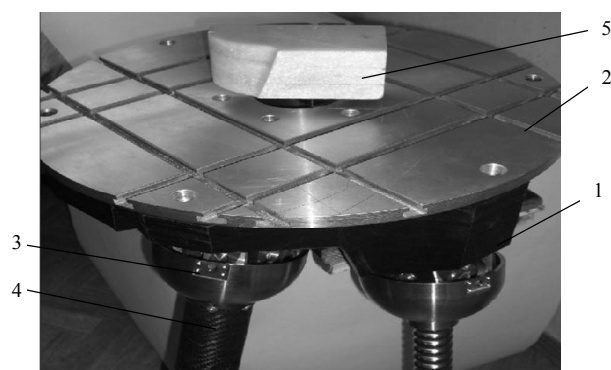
Разработанная конструкция платформы со штангами многокоординатного оборудования: 1 – платформа; 2 – стол; 3 – сферическая опора; 4 – штанга; 5 – деталь, обработанная на станке
